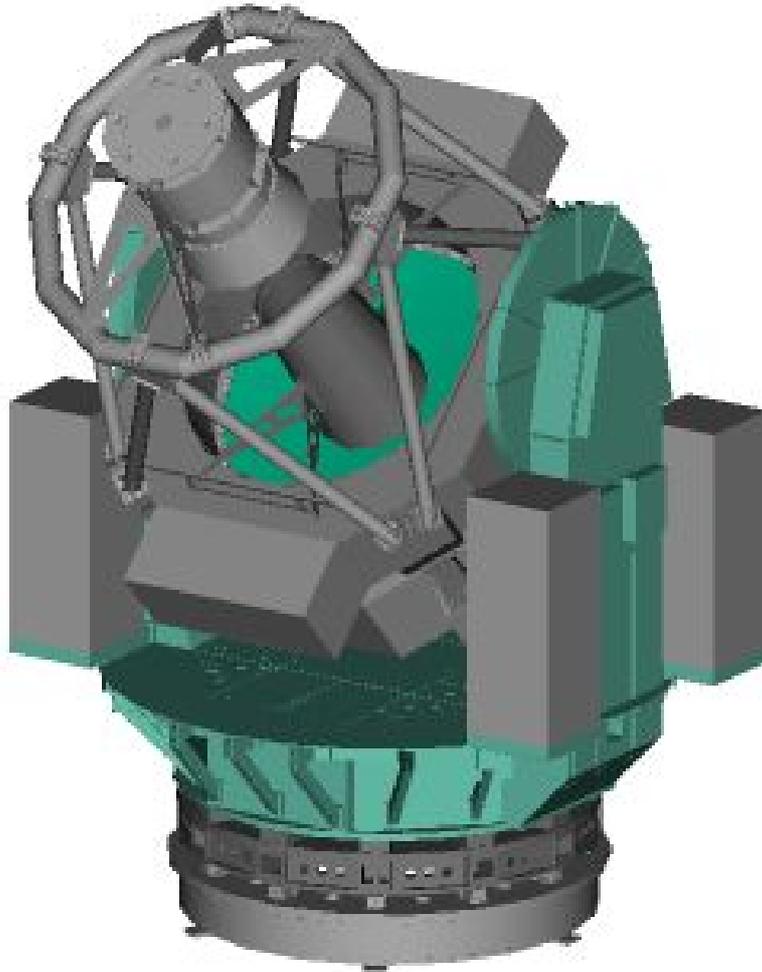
Vista Render del telescopio VST completo di interfaccia verso il pilastro e dei cabinet di controllo. I cabinet sono poi stati rimossi dal telescopio e installati sul pavimento rotante dell'edificio.
